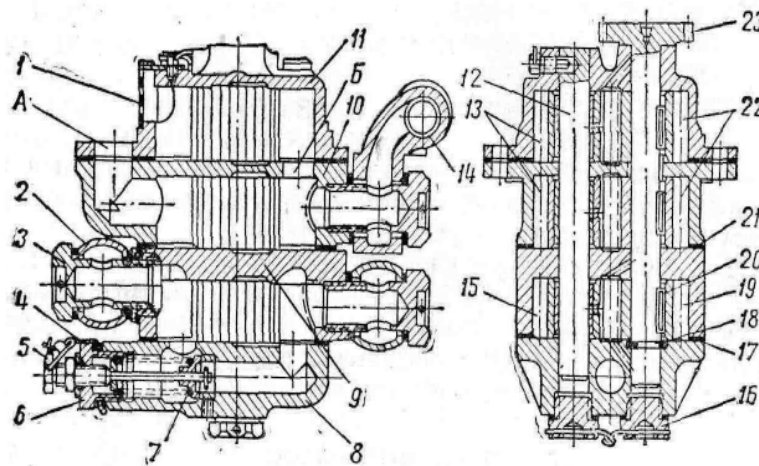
Масляний насос: 1 – сітка; 2 – наконечник; 3 – затиск; 4 – пластинчастий замок редукційного клапана; 5 – стрижень редукційного клапана; 6 – корпус редукційного клапана, 7 – тарілка редукційного клапана, 8 – кришка; 9 – корпус нагнітаючої секції; 10 – корпус нижньої відкачуючої секції; 11 – корпус верхньої відкачуючої секції; 12 – вісь ведених шестірень; 13 – відомі шестірні відкачуючих секцій, 14 – коробки відводу масла в систему; 15 – ведена шестірня нагнітаючої секції; 16 – пробка; 17, 21 – прокладки; 18 – стопорне кільце; 19 – ведуча шестерня нагнітаючої секції; 20 – шпонка; 22 – ведучі шестірні відкачуючих секцій; 23 – ведучий валик с шестірнею
